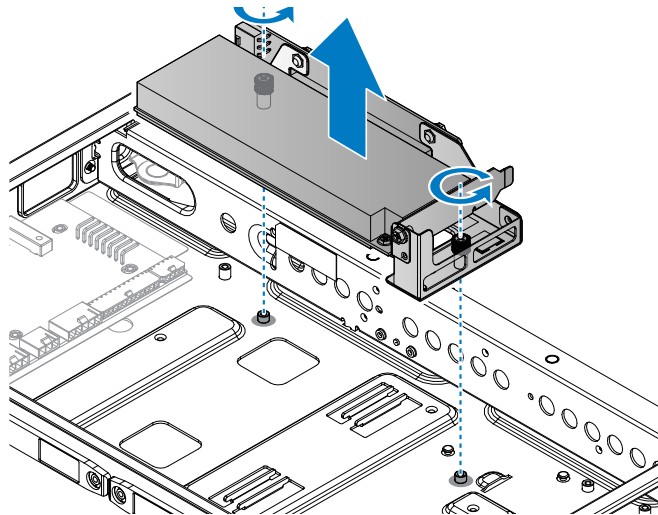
Entfernen der NPIO-Kartenbaugruppe
